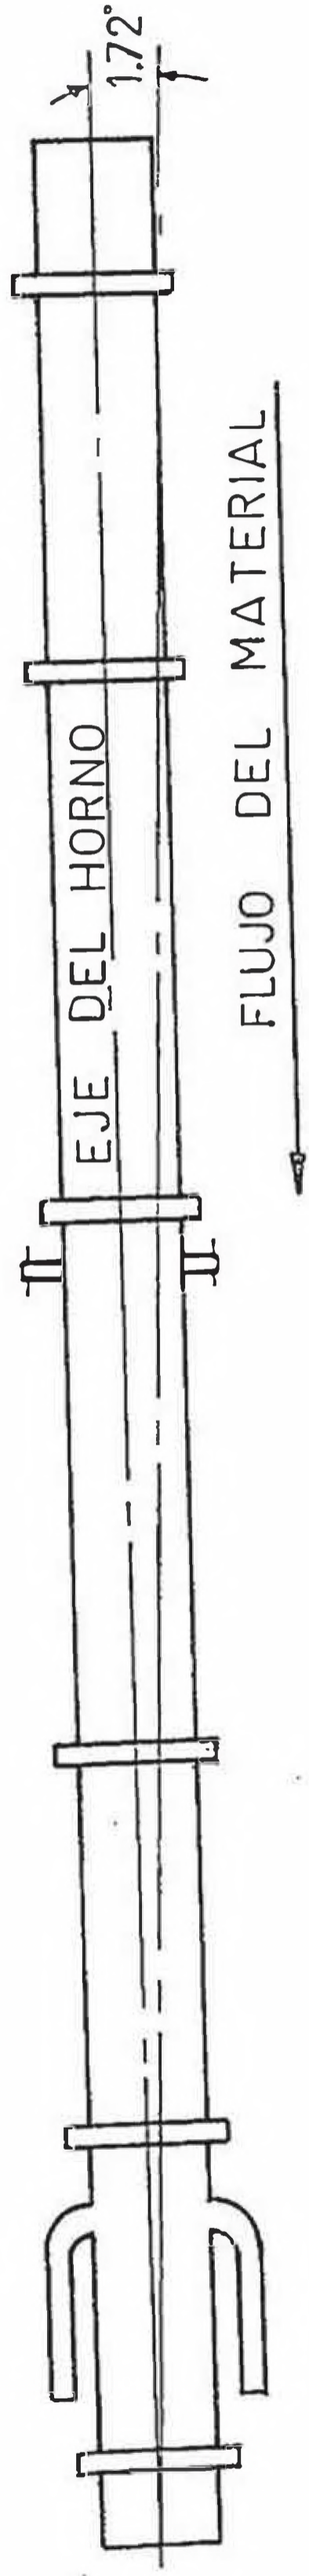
B VISTA DEL HORNO EN EL PLANO VERTICAL
